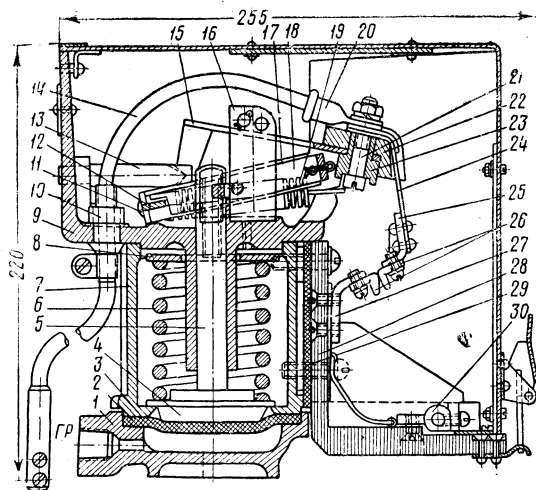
Регулятор давления усл. № АК-6А для мотор-компрессоров
